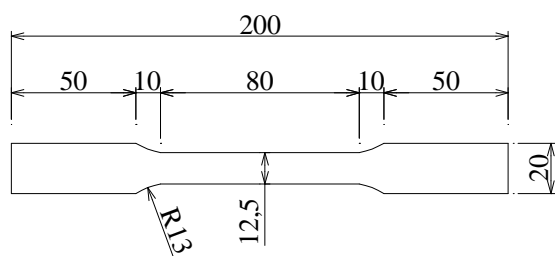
Dimensões dos corpos-de-prova conforme ASTM A370:2009 (dimensões em mm)
